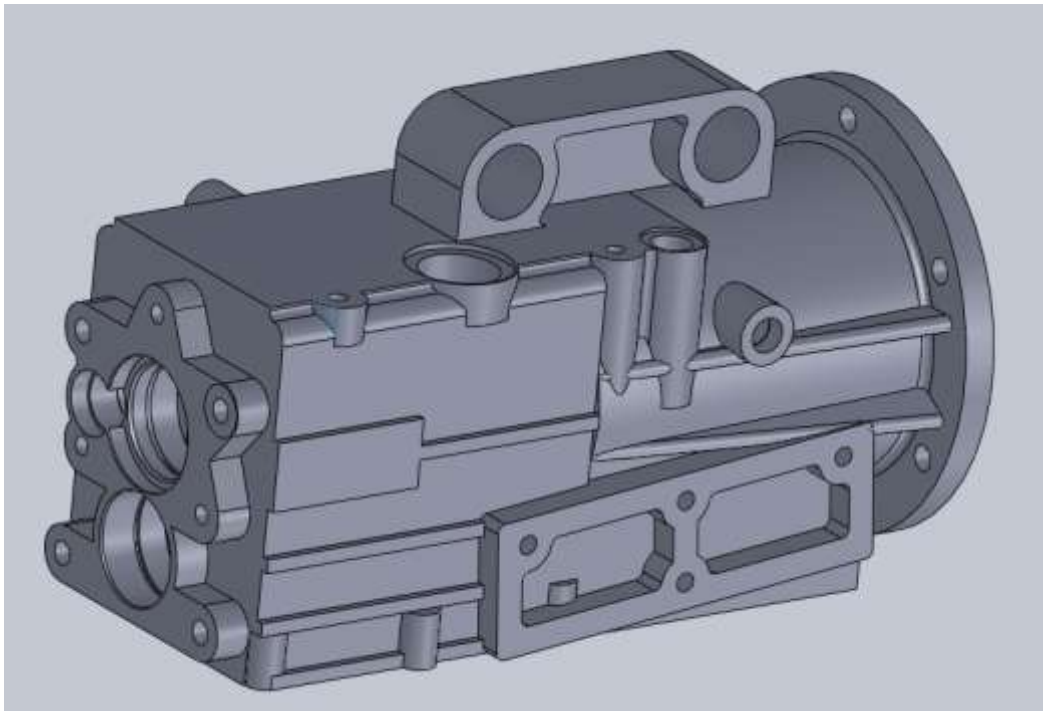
Трехмерная модель детали «Корпус», спроектированная в SolidWorks
